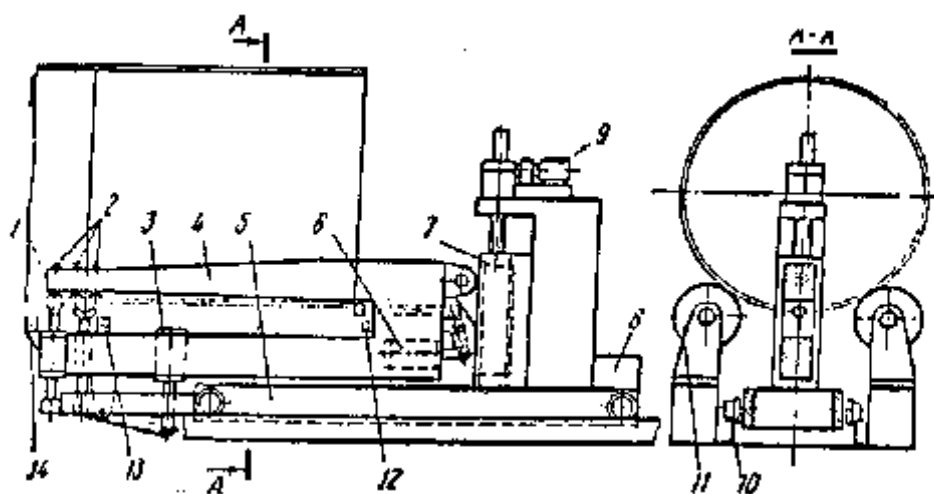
Установка для сборки и прихватки обечаек по кольцевым стыкам
